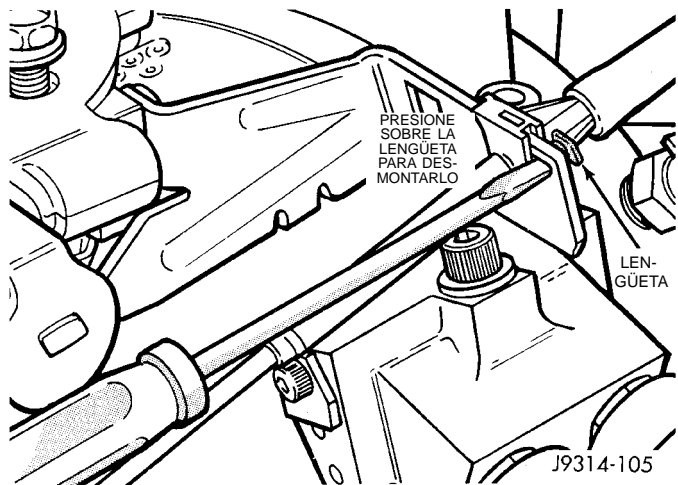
Lengüeta de desenganche del cable—Motores de 5.2L/5.9L—Característica
